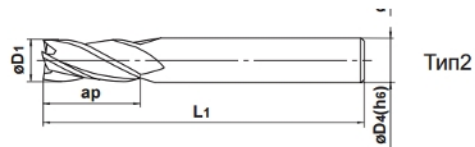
Шпонкова фреза MS4MCD1600E; Матеріал – UWC;
